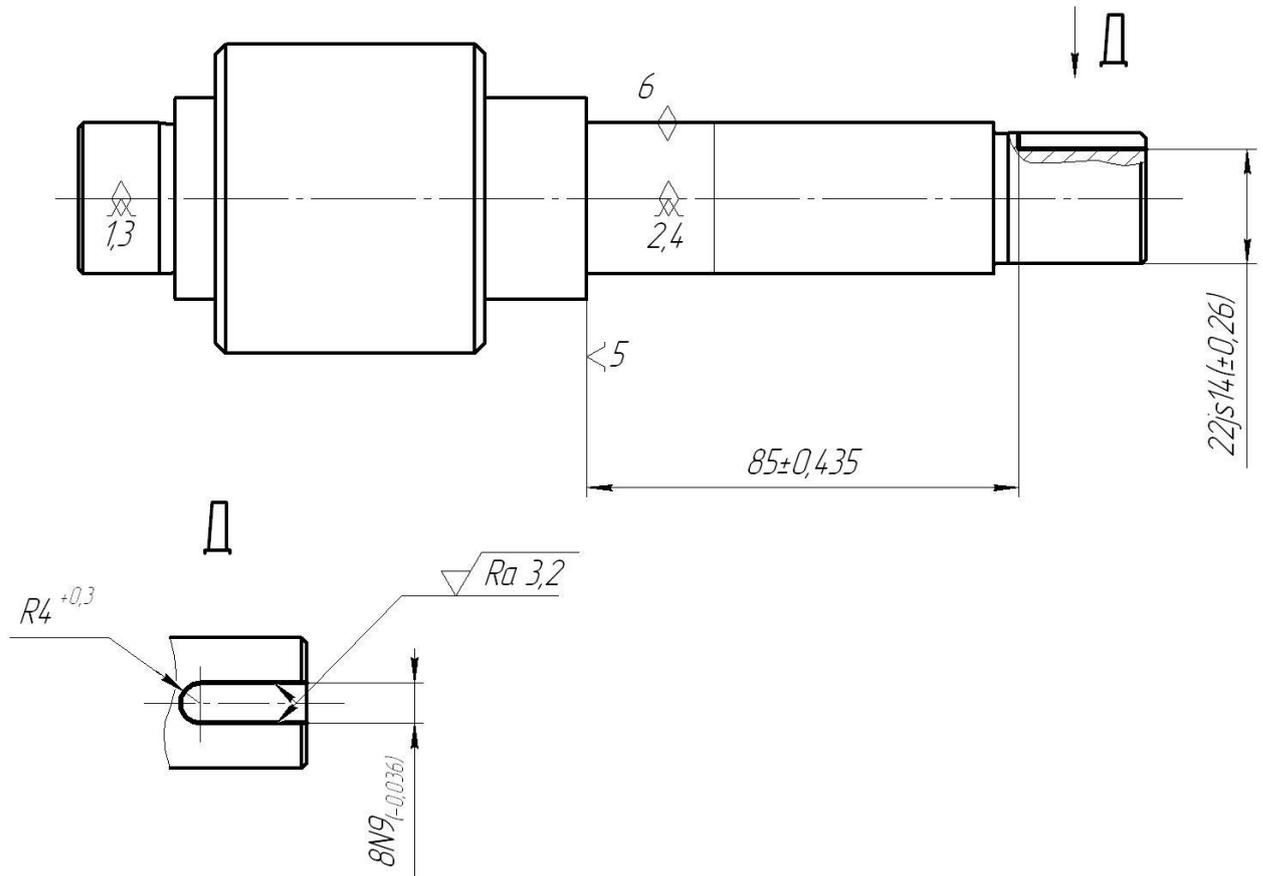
Эскиз шпоночно-фрезерной операции
